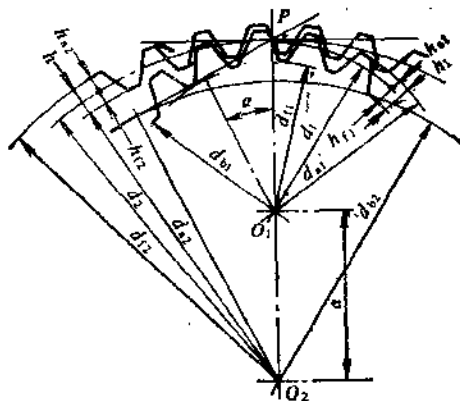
圆柱齿轮传动几何要素（内啮合传动）
